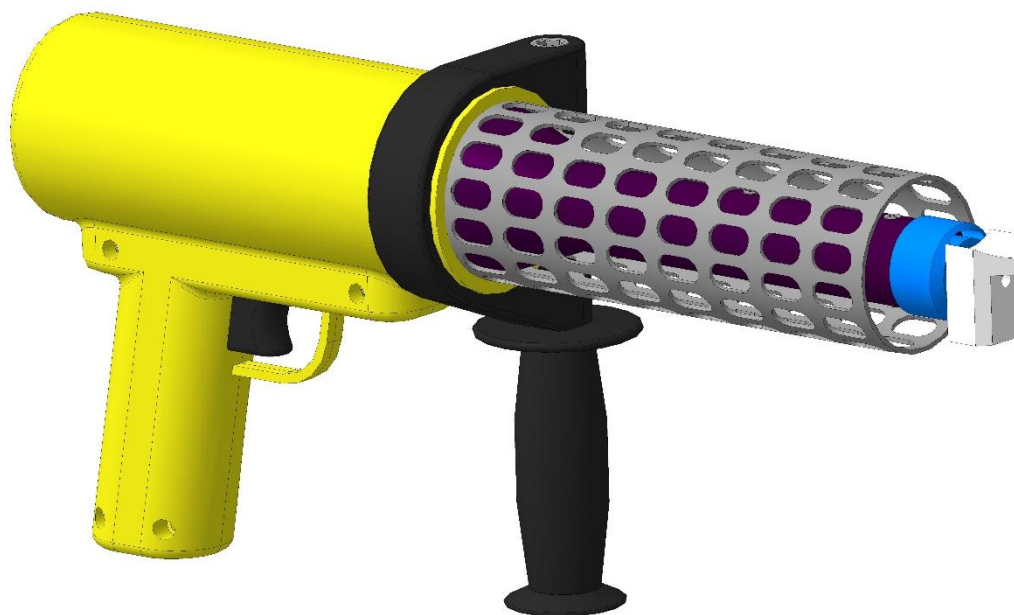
Внешний вид сварочного экструдера.
